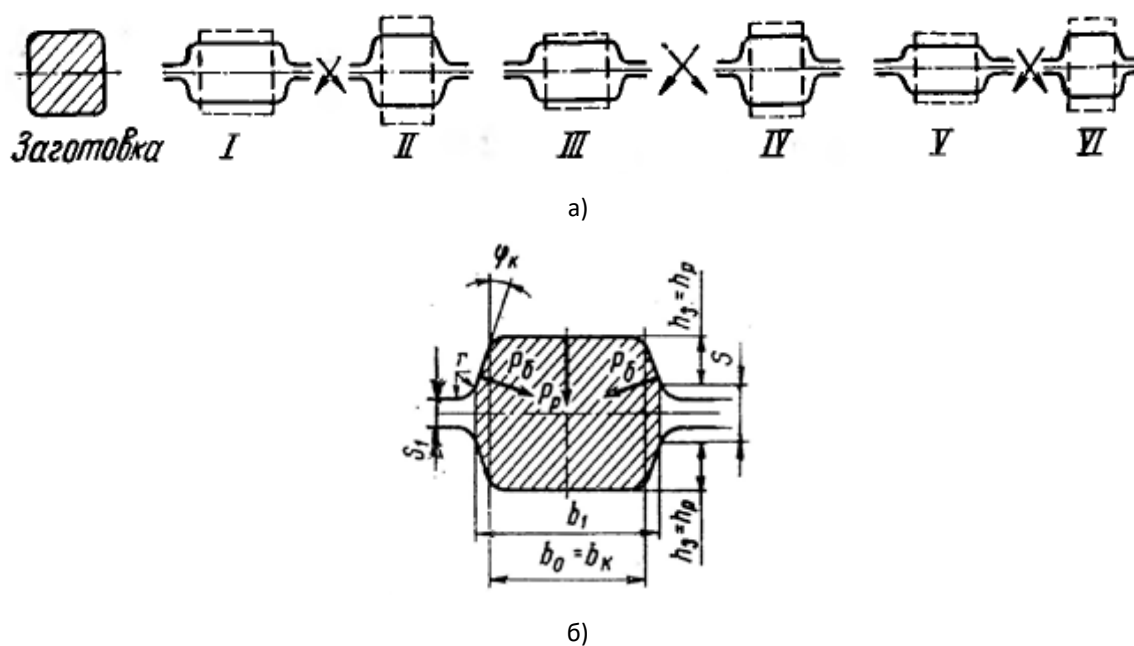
Система прямоугольных (ящичных) калибров (а) и схема дополнительных удерживающих на боковой поверхности калибра (б)
